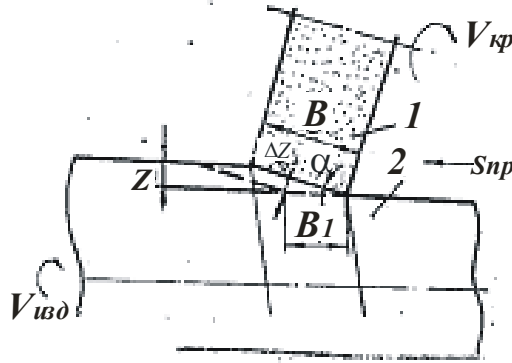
Расчетная схема круглого продольного шлифования: 1 – круг; 2 – изделие
